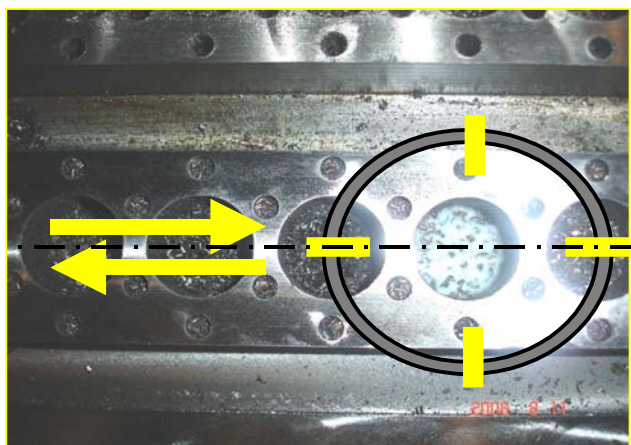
Sentido de usinagem da fresa no blank usinado.
